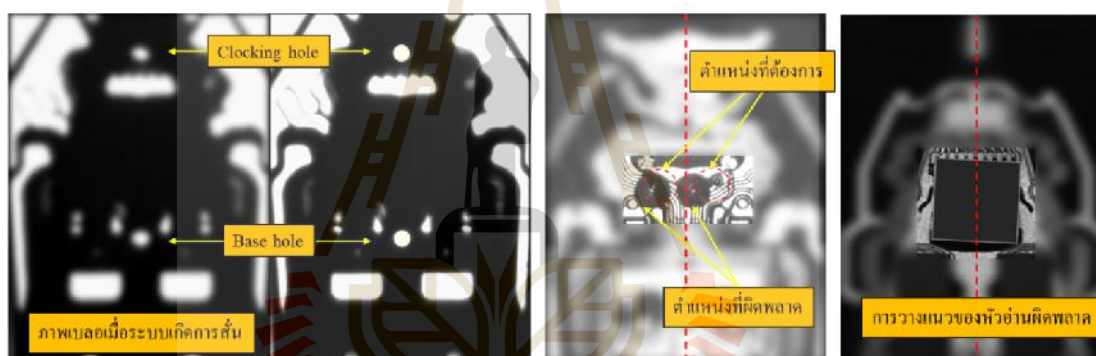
Head Gimbal Assembly (HGA)
